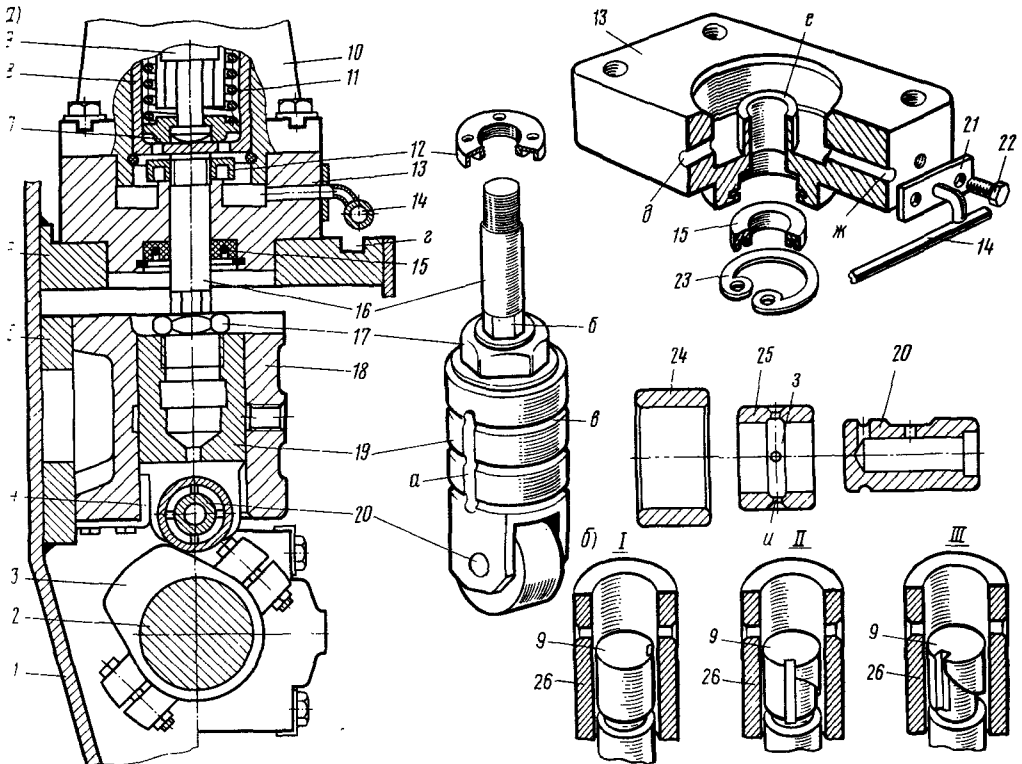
Толкатель топливного насоса (а) и положения плунжера при различной подаче топлива (б): 1 — боковой лист блока; 2 — распределительный вал; 3 — топливный кулачок; 4 — угольник; 5 — фланец; 6 — верхний горизонтальный лист; 7 — тарелка; 8 — стакан; 9 — плунжер; 10 — корпус топливного насоса; 11 — пружина; 12 — отражательная гайка; 13 — бышшка; 14 — сливная трубка; 15 — сальник Гуфери; 16 — регулировочный болт; 17 — контргайка; 18 — корпус толкателей; 19 — толкатель; 20 — палец; 21 — плайка; 22 — болт; 23 — стопорное кольцо; 24, 25 — наружное и внутреннее кольца ролика; 26 — гильза; а — вертикальный паз; б — шестигранник; в, г, з — канавки; д, ж, и — отверстия; е — выступ бышшки
